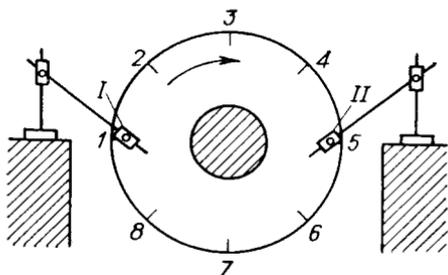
Схема проверки упорного диска на биение двумя индикаторами:
